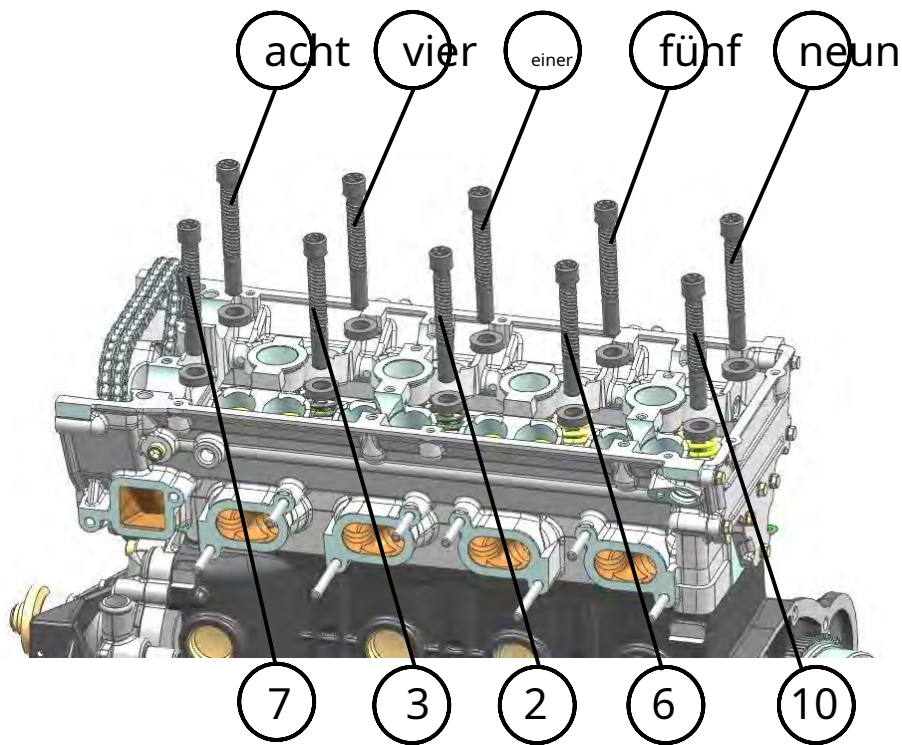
Anzugsreihenfolge für Motor-Zylinderkopfschrauben mit starre (Stahl-)Zylinderkopfdichtung
